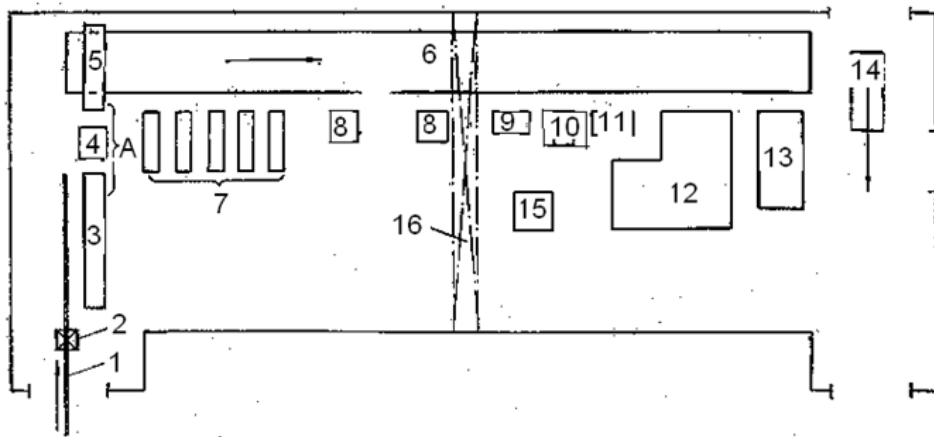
Розташування обладнання трубозаготовчого цеху
